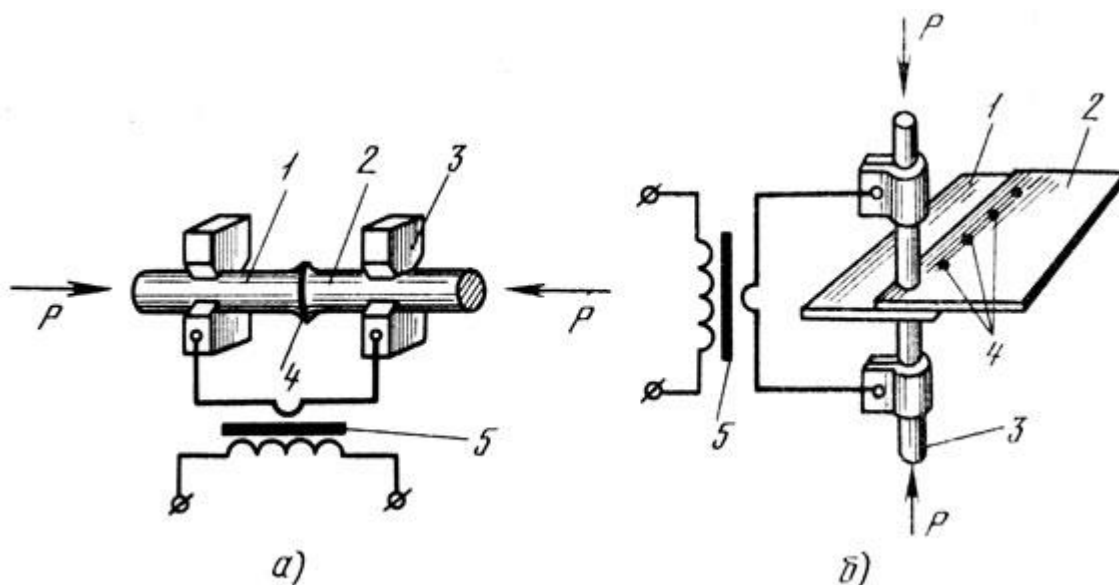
Схема соединения деталей сваркой давлением: а - стыковая контактная сварка, б - точечная контактная сварка; 1 и 2 - свариваемые детали, 3 - медные электроды, 4 - место сварки, 5 - сварочный трансформатор, P - сжимающее усилие
